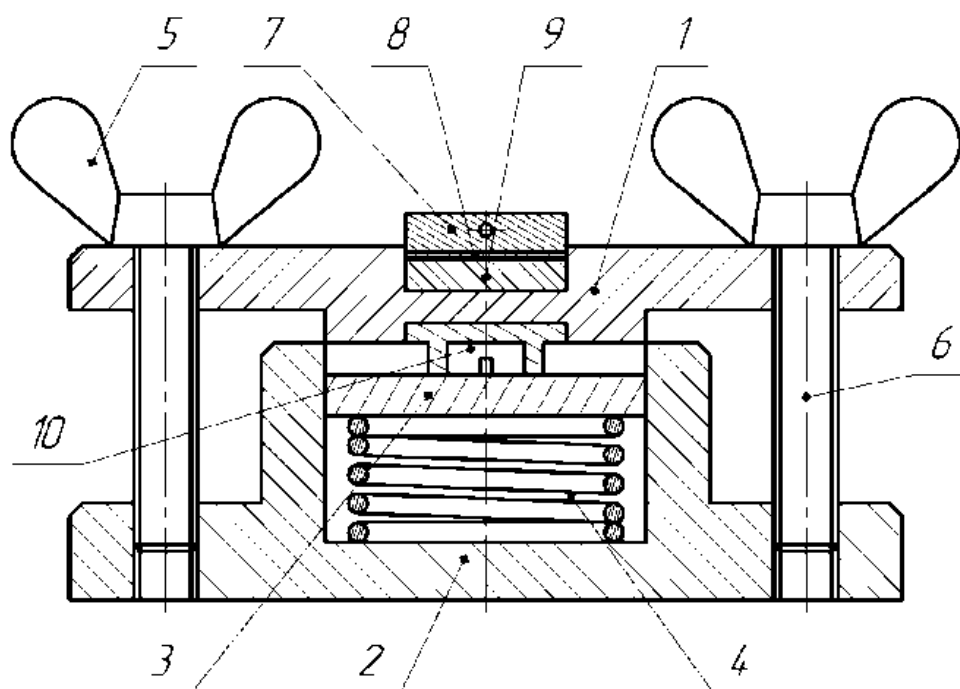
Схема струбцины для нагружения образцов: 1 – плита верхняя; 2 – основание; 3 – планка; 4 – пружина; 5 – гайка барашковая; 6 – винт; 7 – тензодатчик из тепло-непроводящего материала с тензорезисторами; 8 – образец для испытаний
